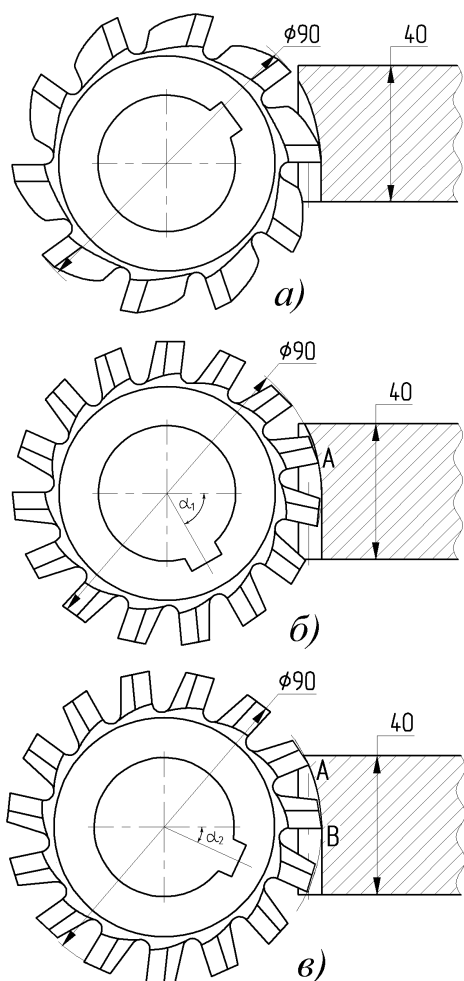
Контакт фрезы с заготовкой в проекции 1
